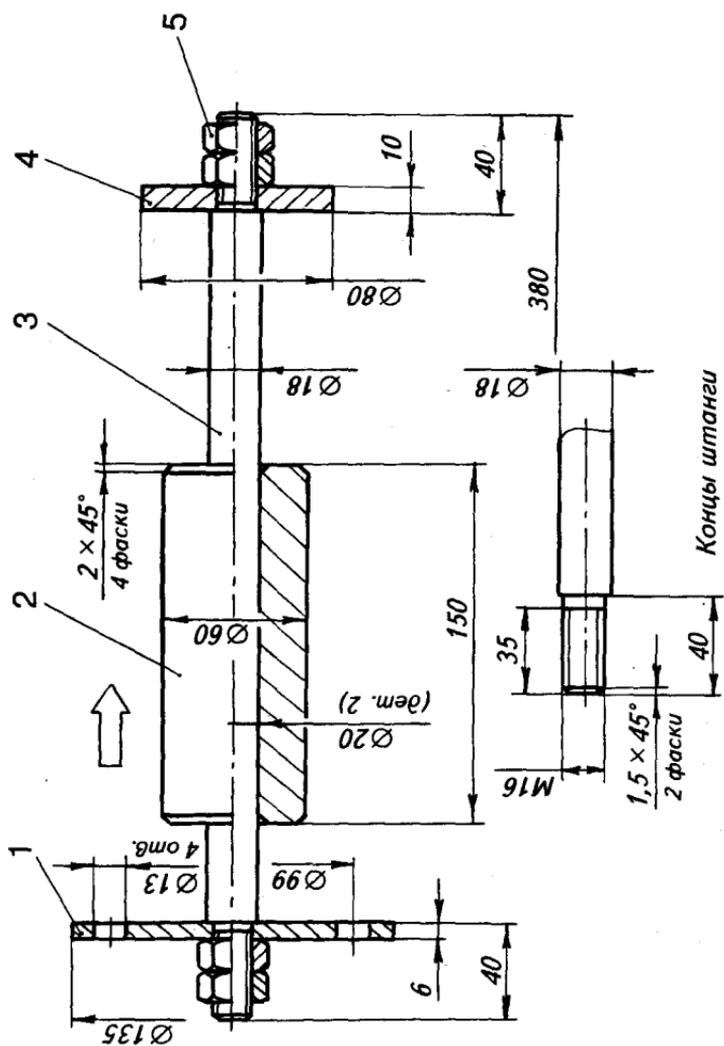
Приспособление для выпрессовывания полуоси: 1 — фланец; 2 — боек; 3 — штанга; 4 — угорная шайба; 5 — гайка (4 шт.).
